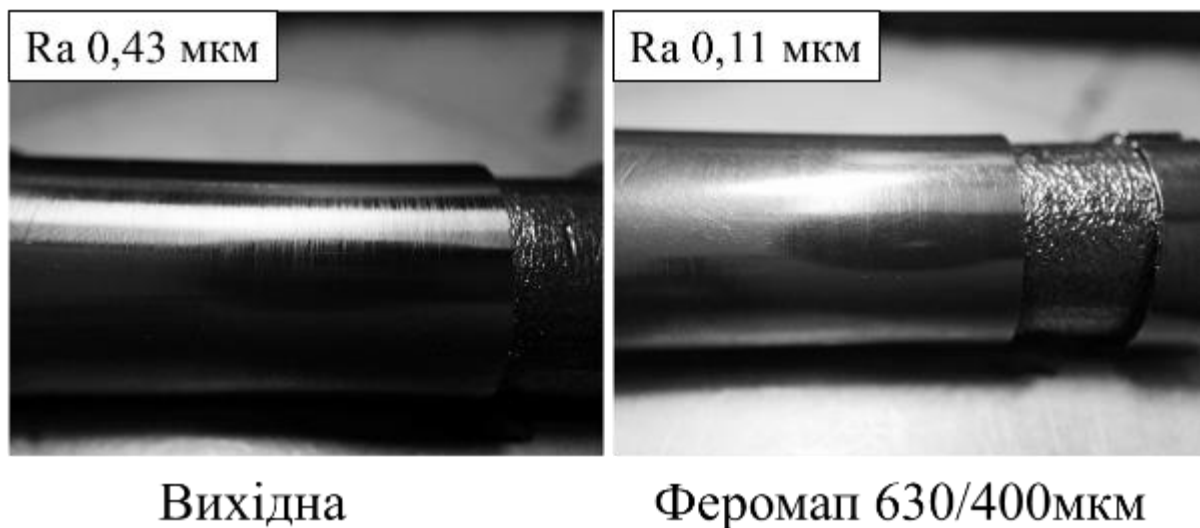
Зовнішній вигляд поверхні після токарного оброблення та після МАО порошком Феромап 630/400 мкм
